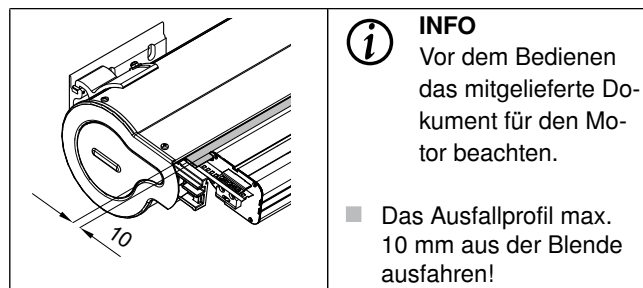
Ausfallprofil ausfahren (alle Maßangaben in mm)
